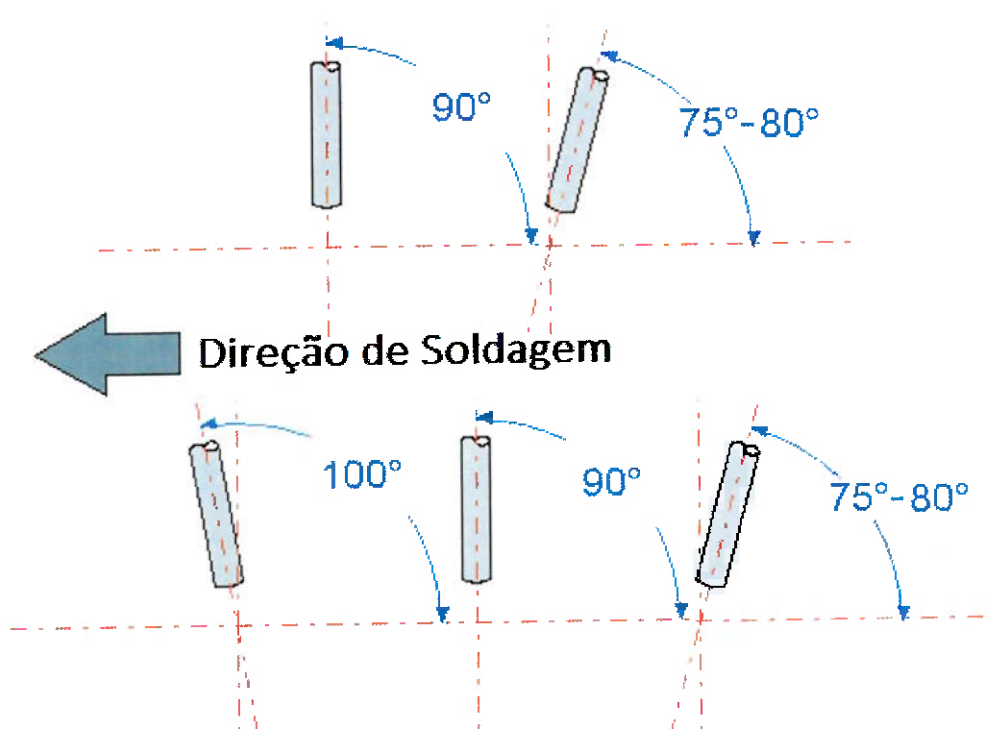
Composições de ângulo de eletrodos para soldagem com Tandem Arc com dois e três eletrodos. [12]
